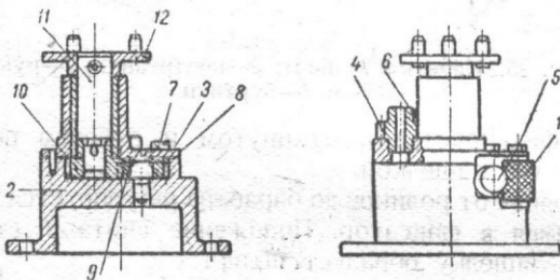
Насос в разрезе: 1—сетка; 2—корпус насоса; 3—вал насоса; 4—прокладка; 5—винт; 6—штуцер; 7—винт; 8—штифт; 9, 10—шестерни; 11—валик; 12—фланец
